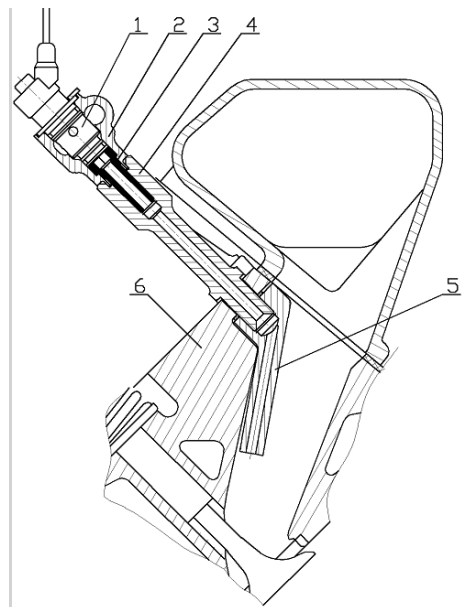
Коллектор газового двигателя КАМАЗ-820.62-300
